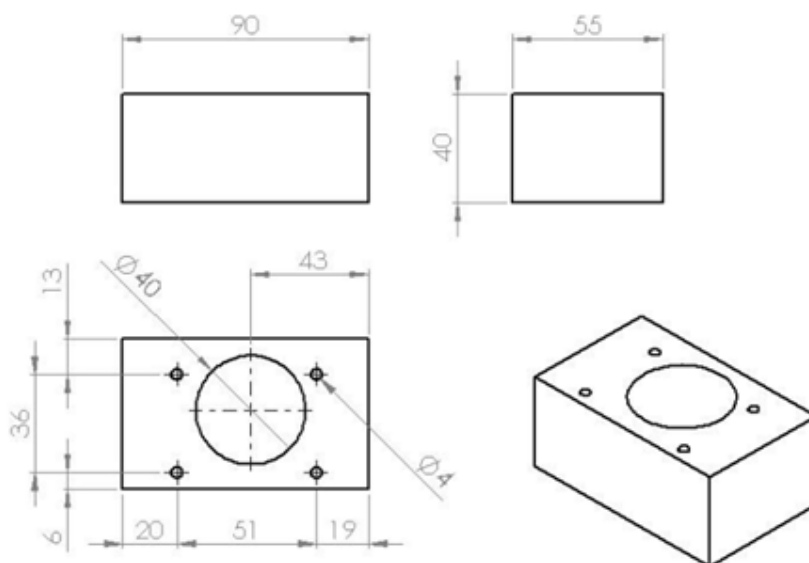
Projeto para fabricação do dispositivo de fixação do bloco do compressor hermético em uma fresadora CNC.
